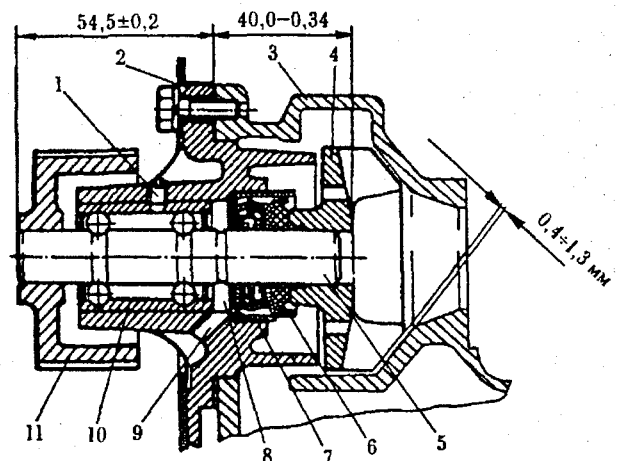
Гидронасос системы охлаждения: 1 – стопорный винт подшипника; 2 – корпус насоса; 3 – блок цилиндров; 4 – крыльчатка; 5 – валик подшипника; 6 – упорное уплотнительное кольцо; 7 – манжетное уплотнение; 8 – канавка; 9 – отверстие; 10 – подшипник; 11 – шкив
